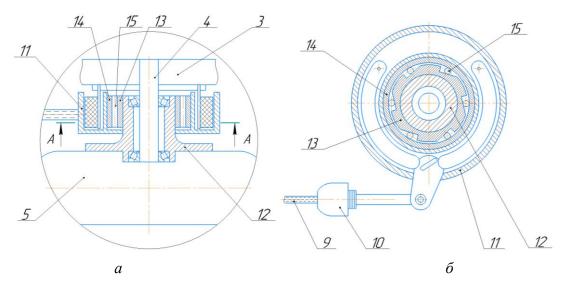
Тормозной механизм колеса прицепа: a – вид сверху;  $\delta$  – вид сбоку
